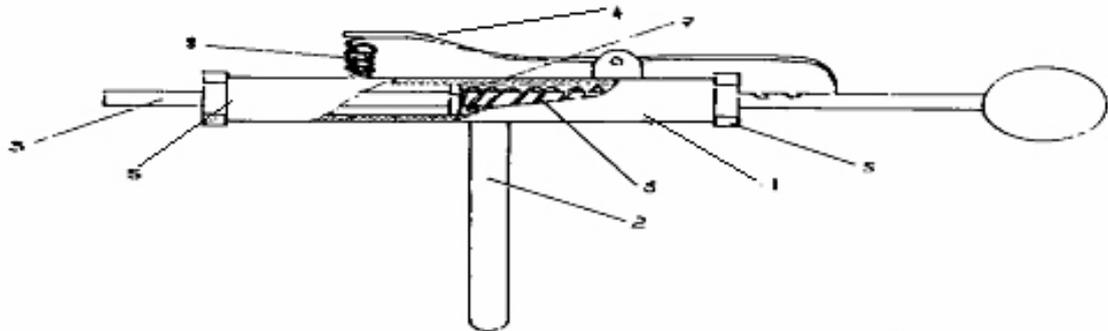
Схема ударника для нанесения дозированной ЧМТ мелким экспериментальным животным. 1-Корпус ударника; 2-Ручка; 3-Ударный стержень; 4-Спусковой крючок; 5-Фиксирующая заглушка корпуса; 6-Пружина ударника; 7-Фиксатор пружины; 8-Пружина спускового механизма.
